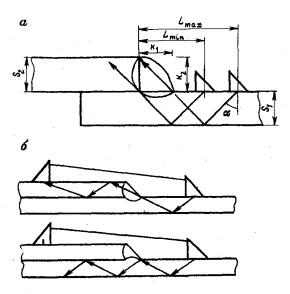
Схемы прозвучивания сварного соединения внахлестку
